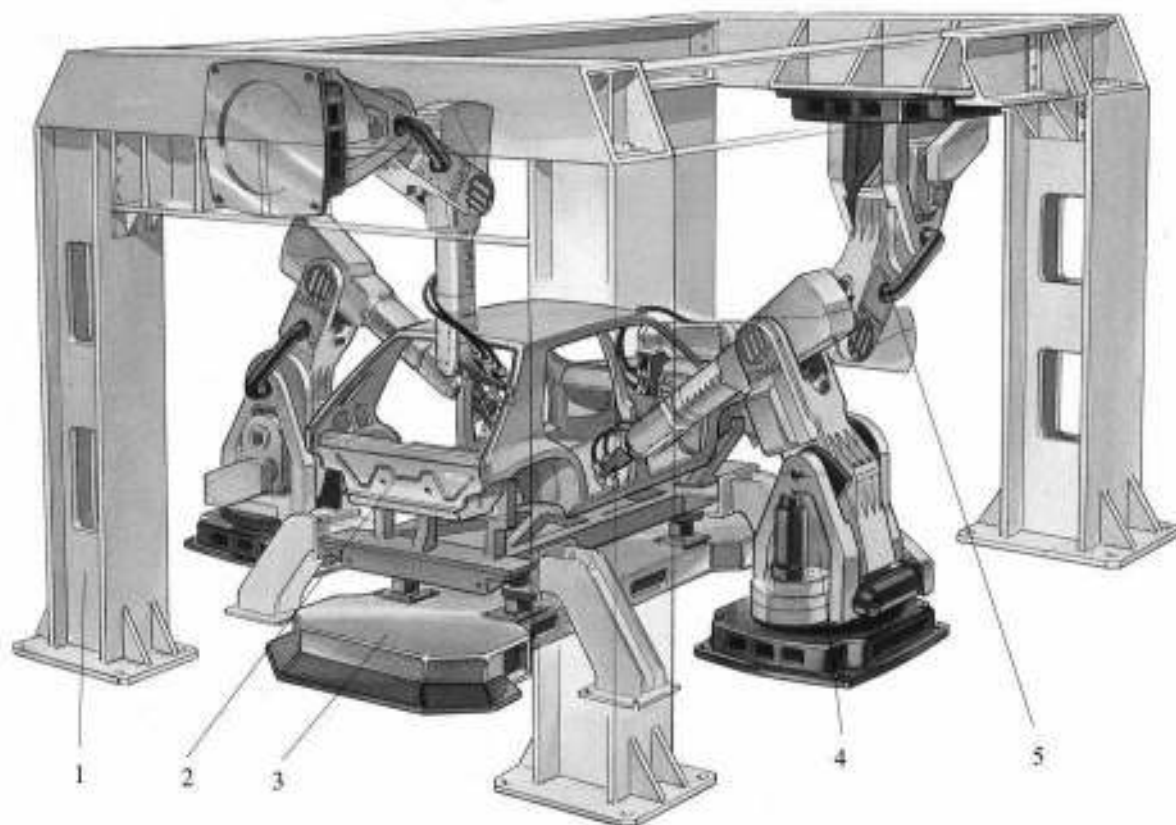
Сварочный РТК для кузова автомобиля
